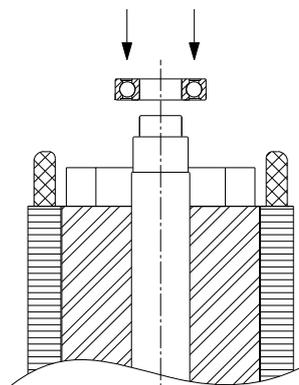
Сборка верхнего подшипника, KPL 500-800
